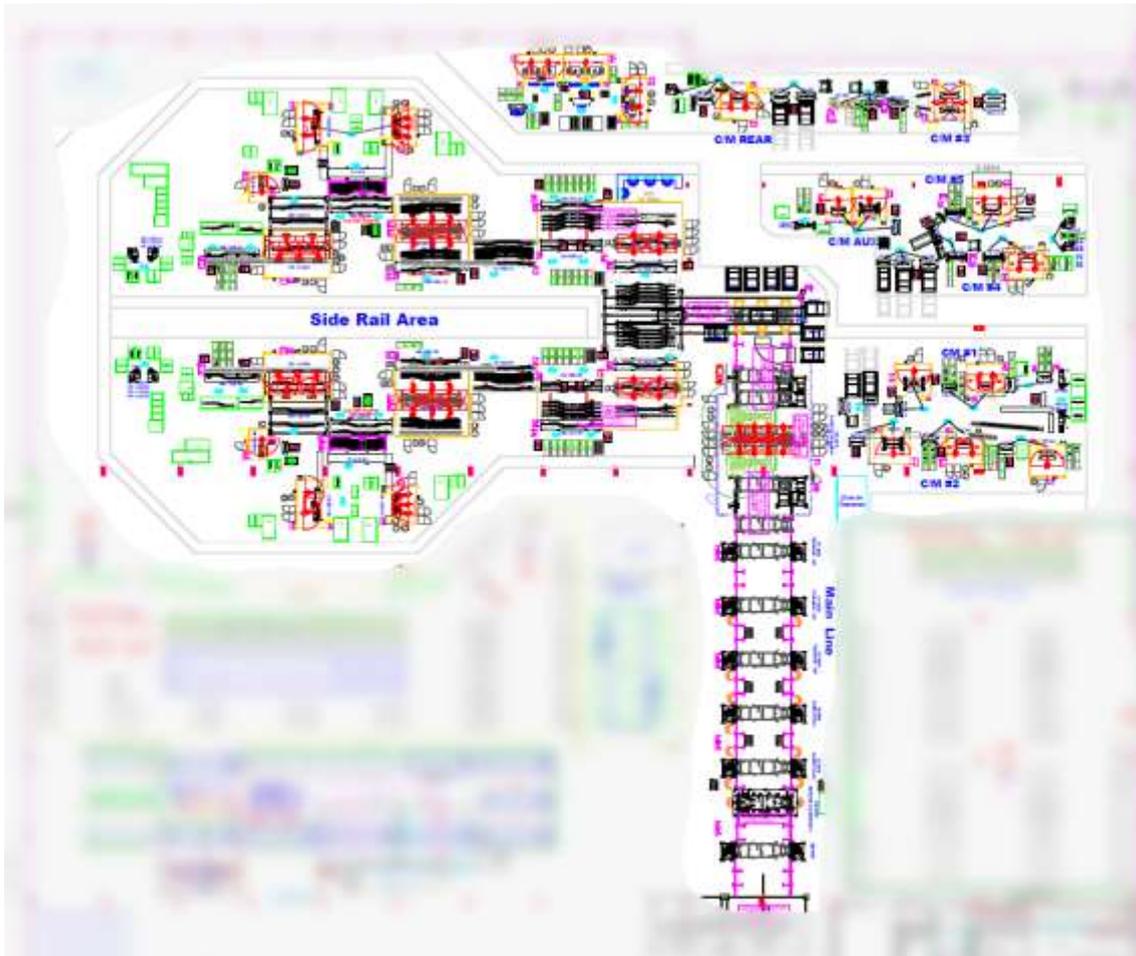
Lay out Completo de la línea de soldadura y ensamble de Toyota. Provisto por Metalsa.
